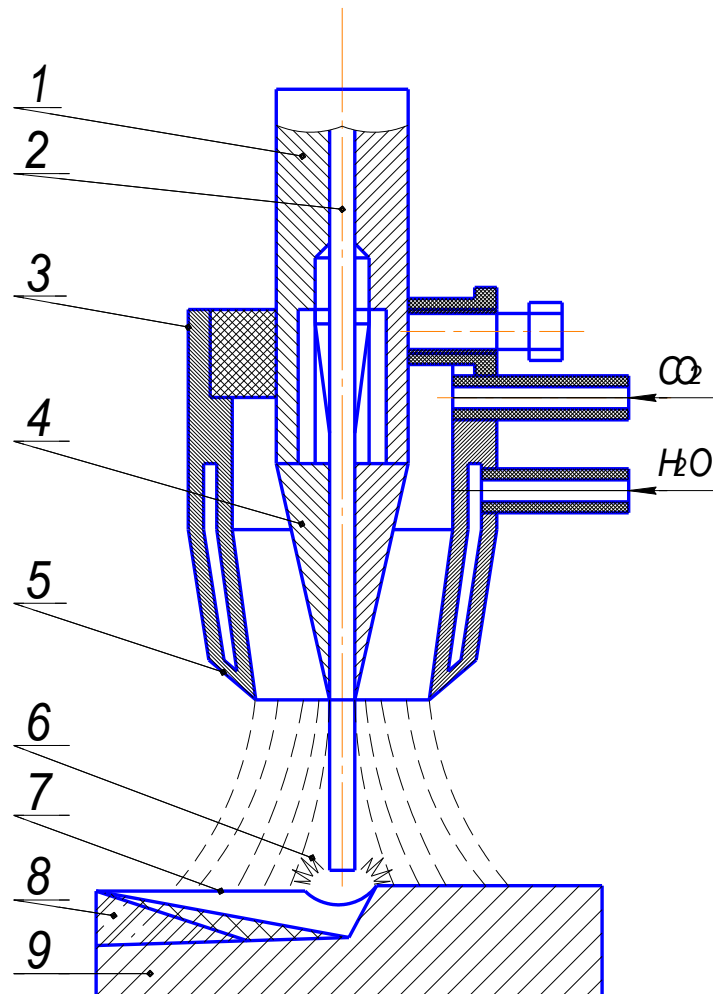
Схема наплавлення зовнішньої поверхні:
